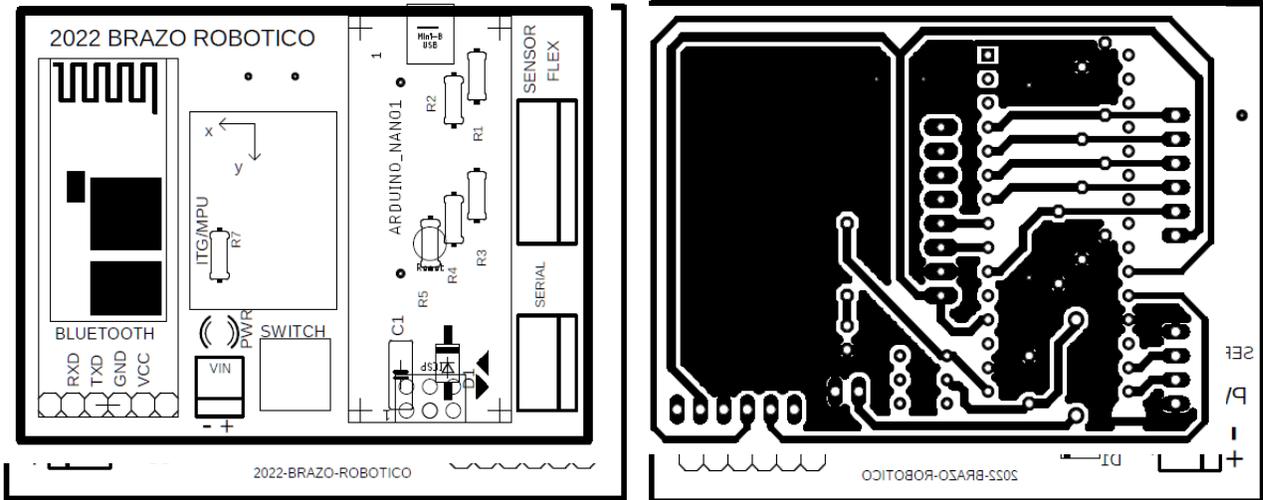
Diseño de la PCB esclavo (Elaboración propia)
